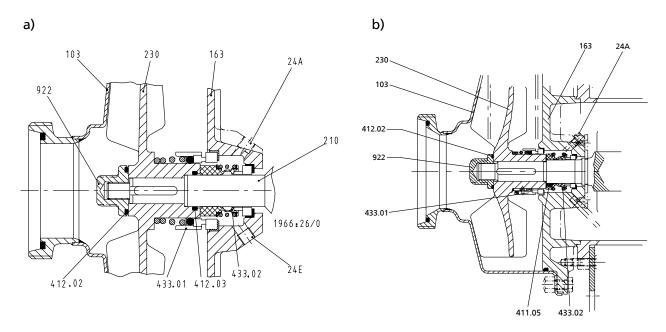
Doppelgleitringdichtung a) mit O-Ring (Baugrößengruppe I) b) mit V-Ring (Baugrößengruppe II)
